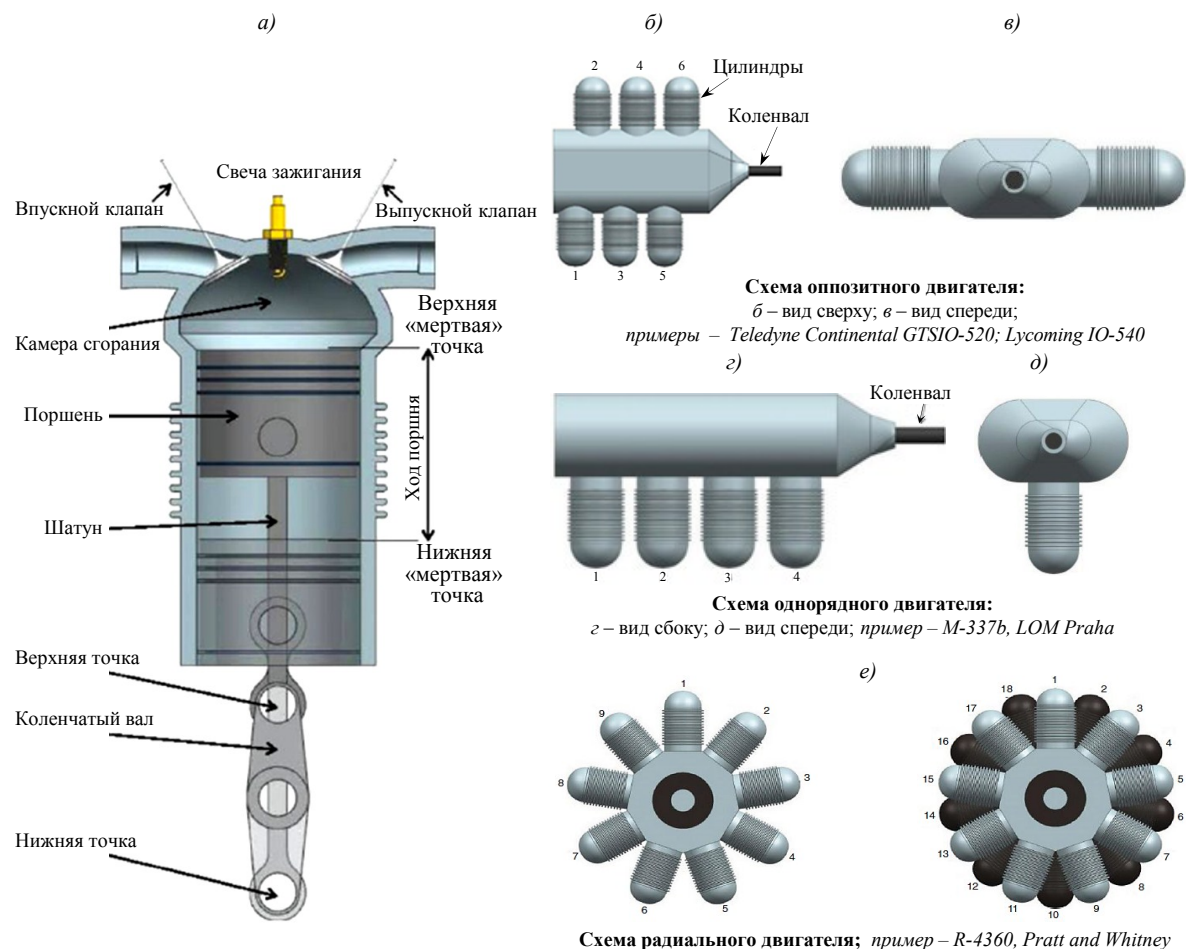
Принципиальная схема поршневого двигателя (а) и схемы расположения цилиндров (б–е) [24]
